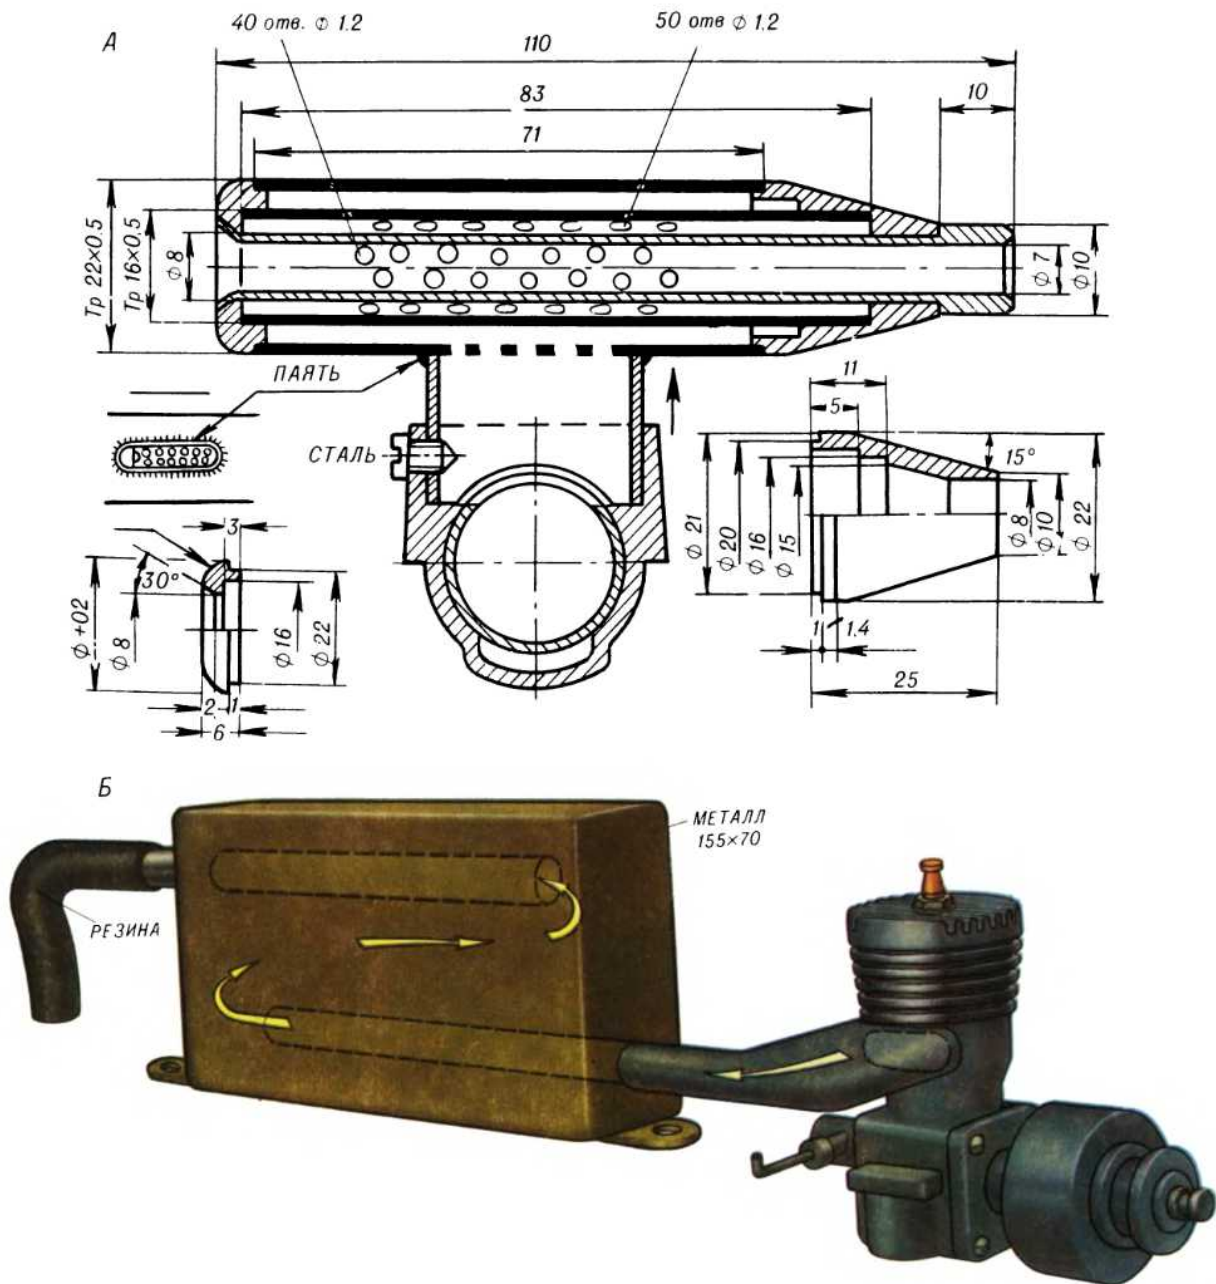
Глушители: А — цилиндрический; Б — коробчатый.
